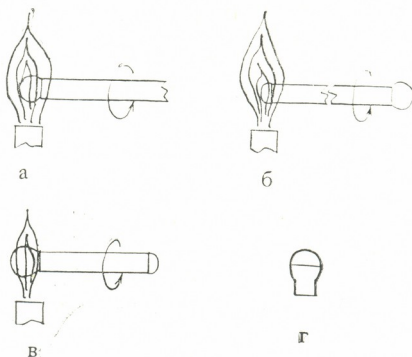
Изготовление лабораторного варианта корпуса для полупроводниковых приемников света. а) образование микролинзы на стеклянном капилляре; б) запаивание второго конца капилляра; в) образование стеклянного корпуса ППС; г) готовый корпус
